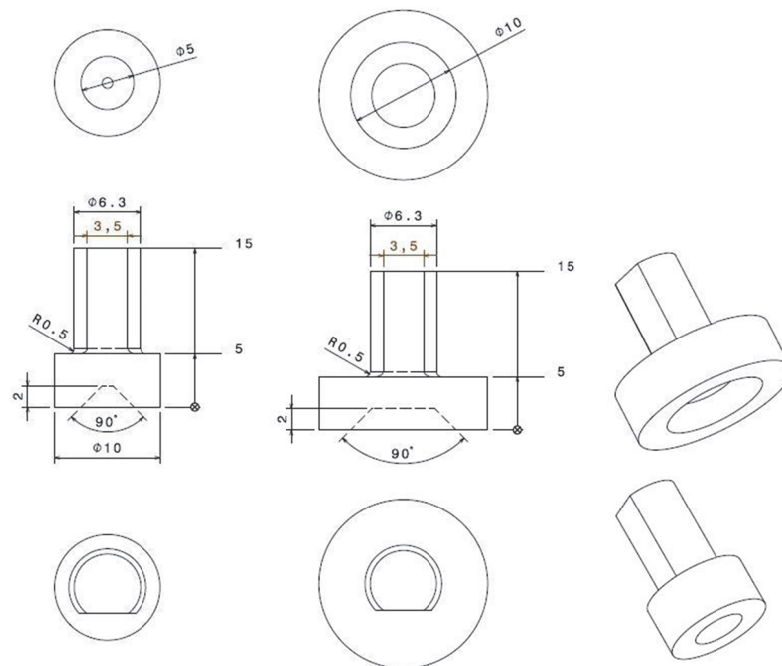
Konstruktionszeichnung der Kugelaufnehmer für die Kantenprüfmaschine ET500.
